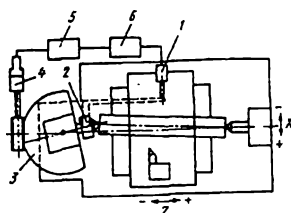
Схема механізму корегування положення осі шпинделя токарного верстата при обробці заготовки
